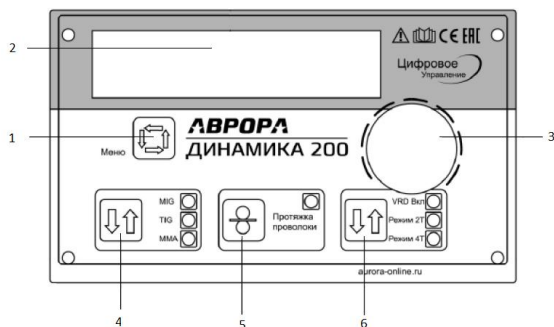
Панель управления: 1 – меню только для сварки MIG (коррекция сварочного напряжения, коррекция индуктивности, выбор диаметра проволоки); 2 – светодиодный цифровой дисплей; 3 – ручка настройки параметров сварки; 4 – выбор вида сварки (MIG, TIG, MMA); 5 – протяжка проволоки; 6 – режим работы горелки MIG (2Т, 4Т).
